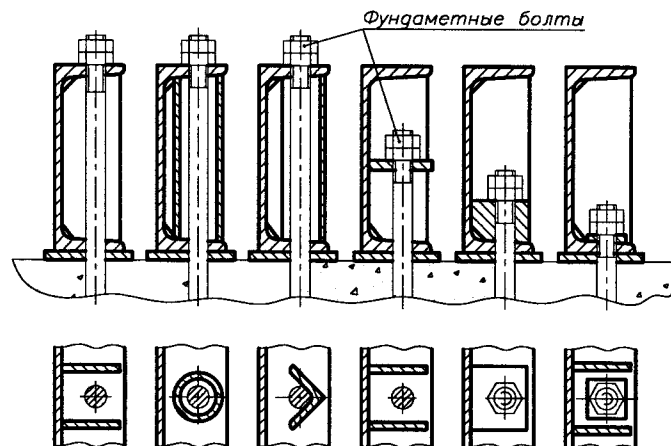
Варианты установки в раме фундаментных болтов
